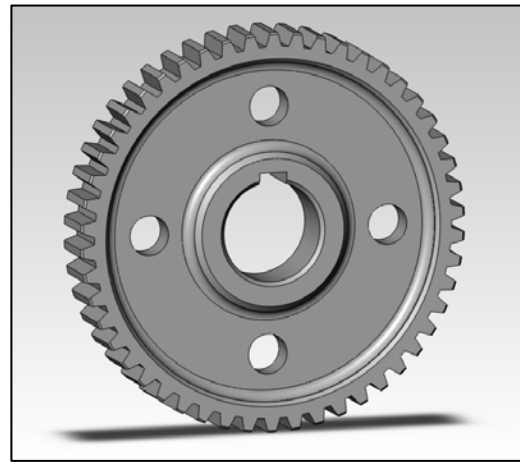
Трехмерная модель детали «зубчатое колесо»
